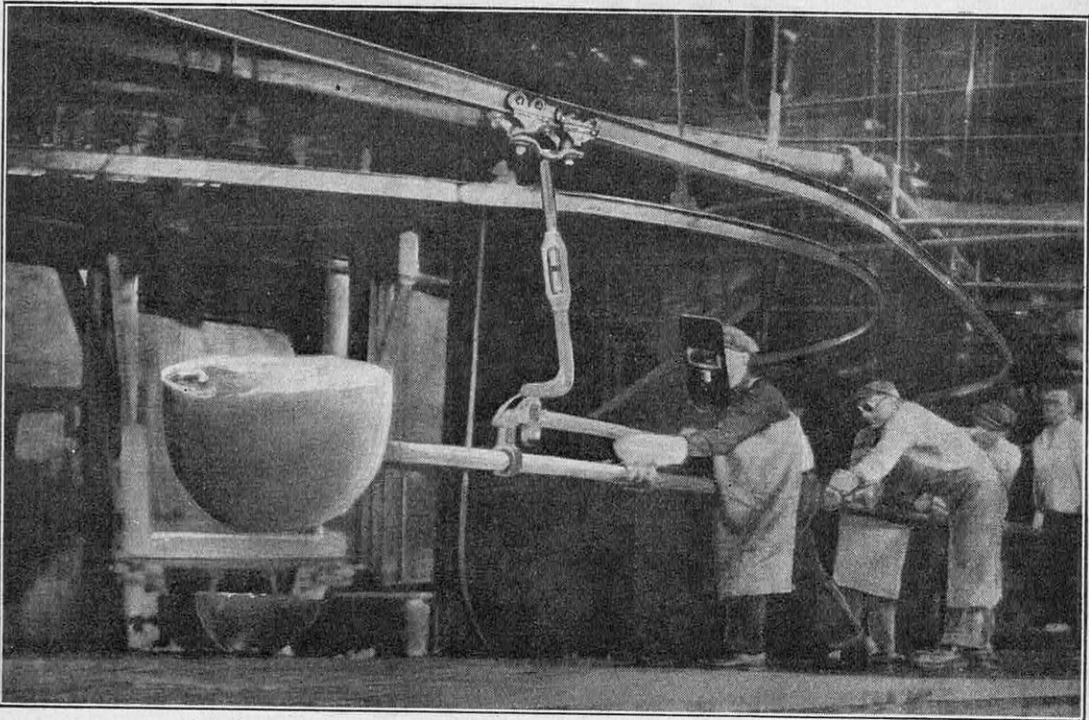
COMMENT ON COULE LE VERRE POUR FAIRE DES GLACES DE GRANDES DIMENSIONS
